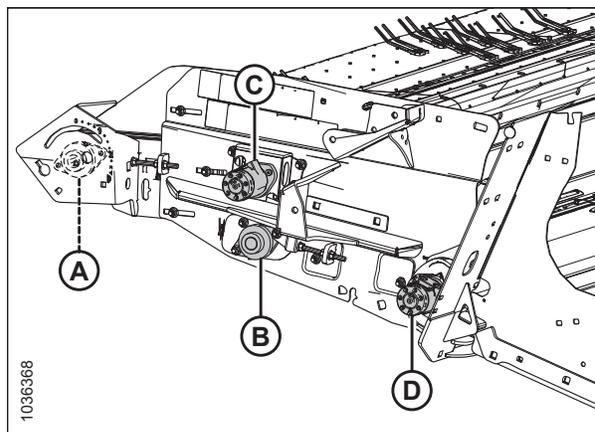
Rodamientos de rodillos de lona: lado izquierdo
